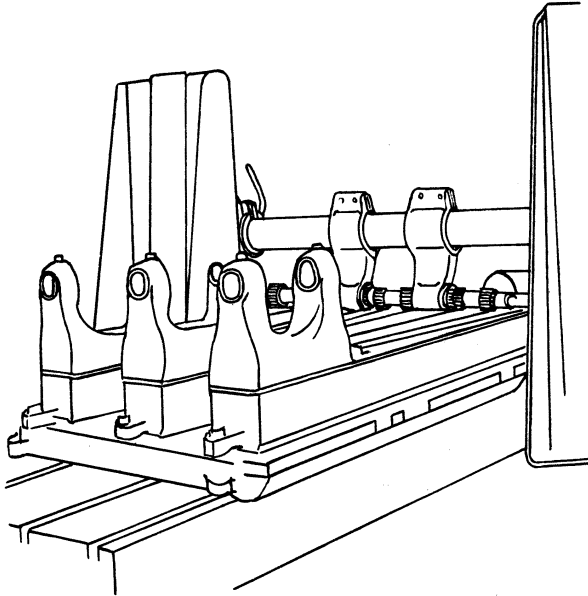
Das Fräsen mit drei gleichen Fräsesätzen.
